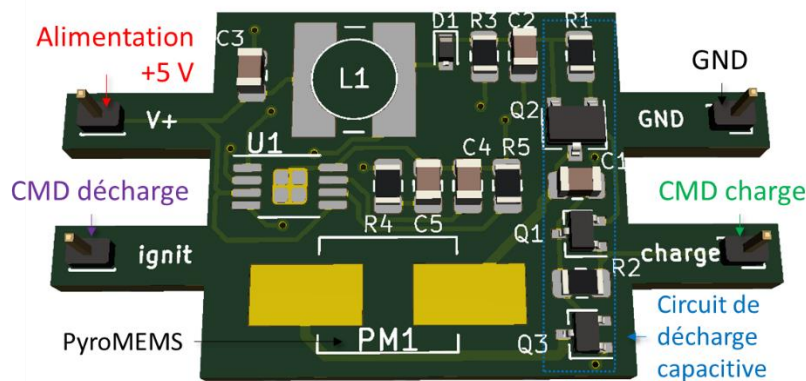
Vue 3D du PCB d'initiation de l'USD\_V2
